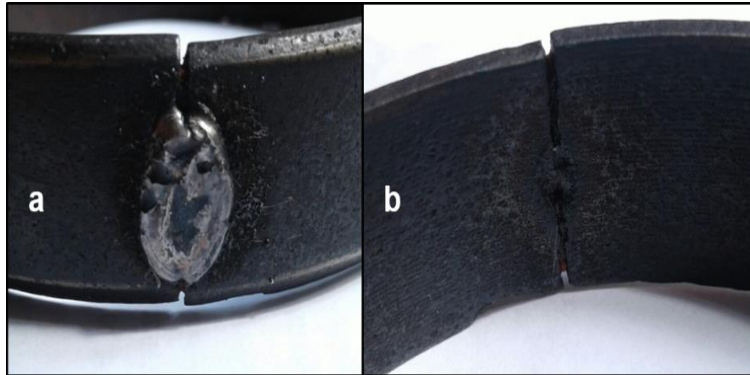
Fotografía de la soldadura aplicada a una fundición gris después de un ensayo de doblado manual.
